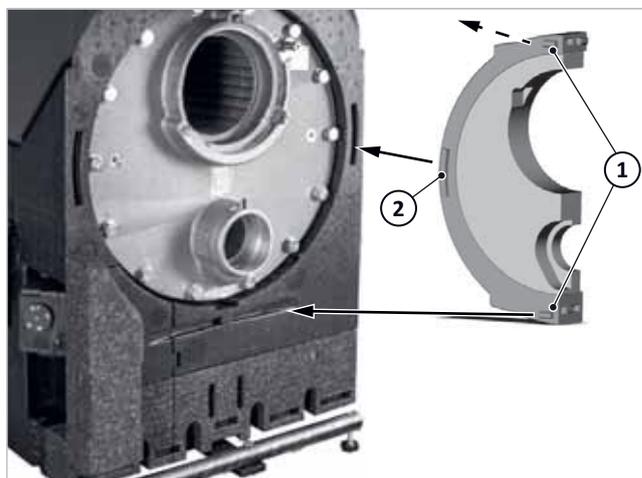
Isolamento anteriore della flangia (a destra, vista posteriore) con le molle di arresto
